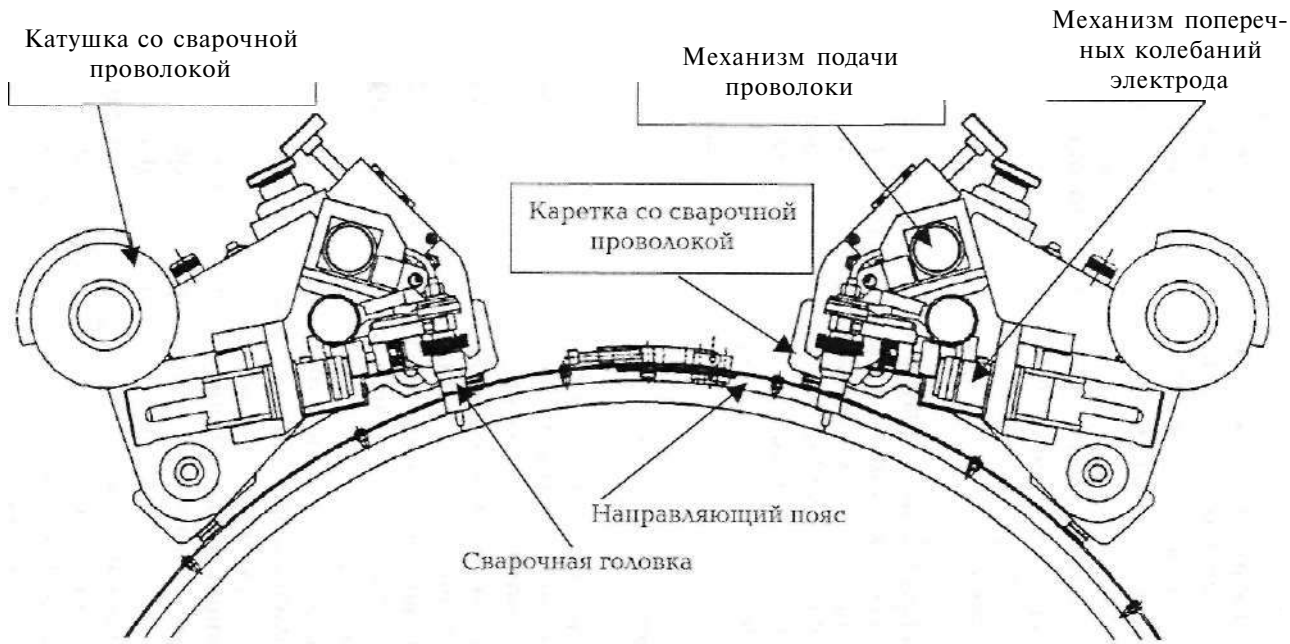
Наружный сварочный аппарат CRC-Evens (схема)
